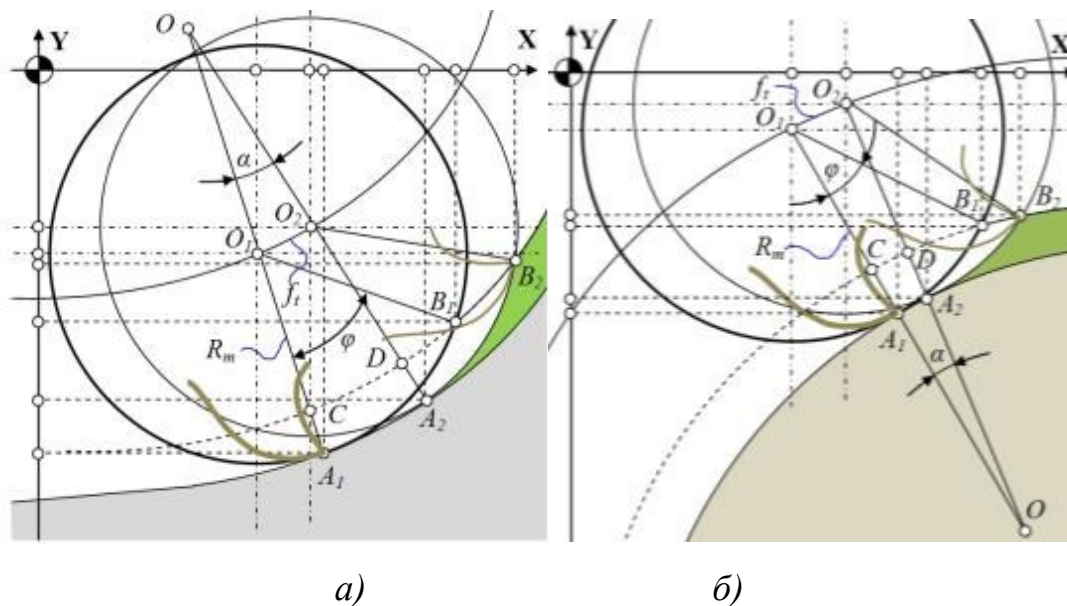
Взаємодія фрези та заготовки: а) – обробка увігнутої поверхні;
